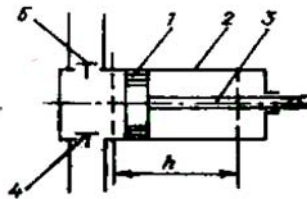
Схема вільновихорного нагнітача: 1 – робоче колесо; 2 – корпус
